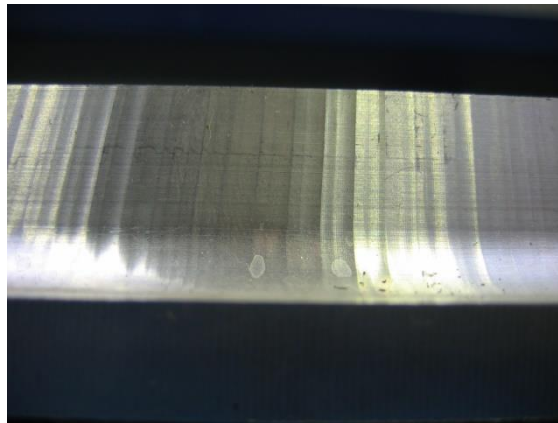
«Вибрационный след» при обработке боковой поверхностью фрезы образца - изделия: скорость вращения шпинделя $S = 18000$ об/мин, подача $F = 2000$ мм/мин, обрабатываемый материал – ДТ 16 М с термообработкой, режущий инструмент цилиндрическая фреза с сферическим закруглением из быстрорежущей стали и винтовой спиральной канавкой $\varnothing 16$, $Z = 2$.
